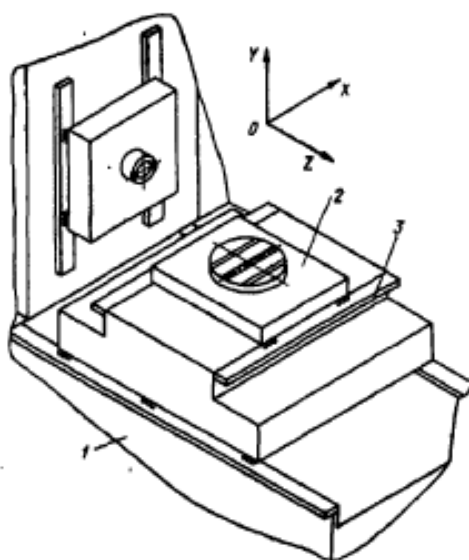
Схема компоновки станка ОП2В04АМФ4 [13]
